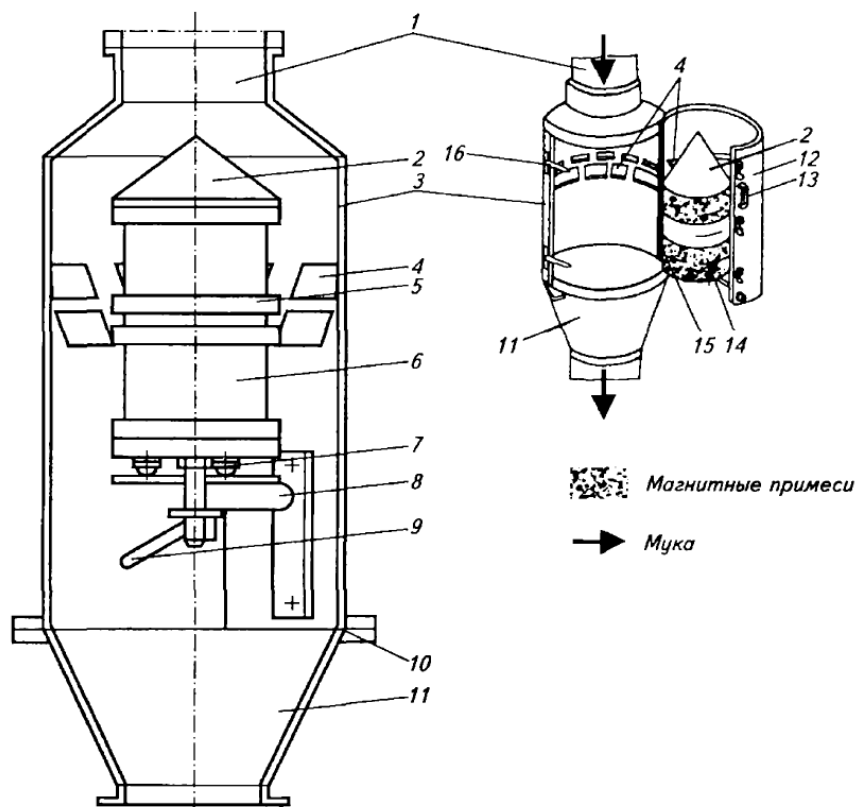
Магнитный сепаратор УИ-БММ:
